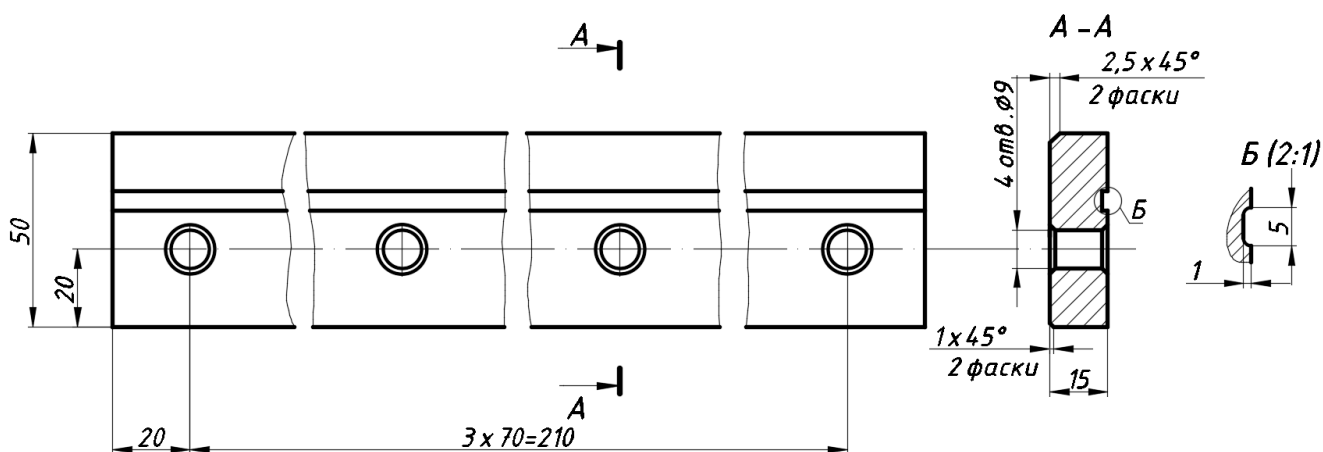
Образец выполнения чертежа детали регулировочной планки с направляющими.
